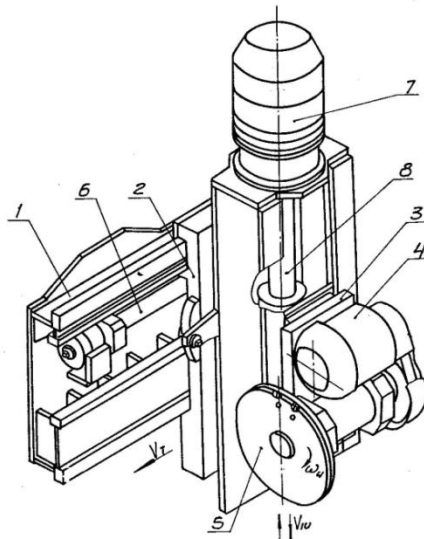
Принципиальная конструкция одношпиндельного спецуппорта к вертикально-зубофрезерному станку мод. 5А342
